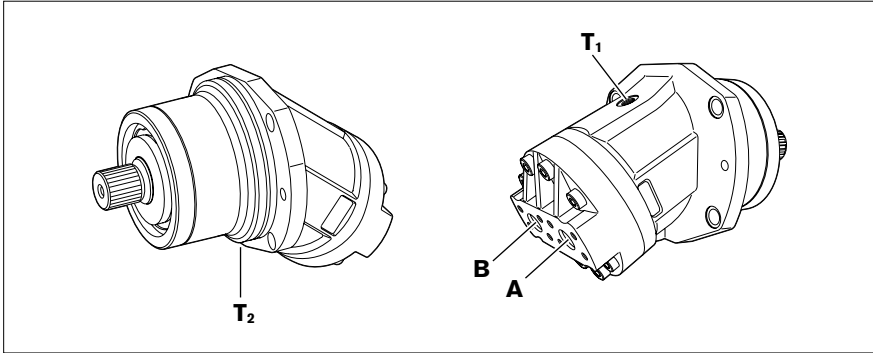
Vue d'ensemble des raccords A2FE, dimension nominale 250 à 355, plaque de raccordement 01, raccords de service arrière
